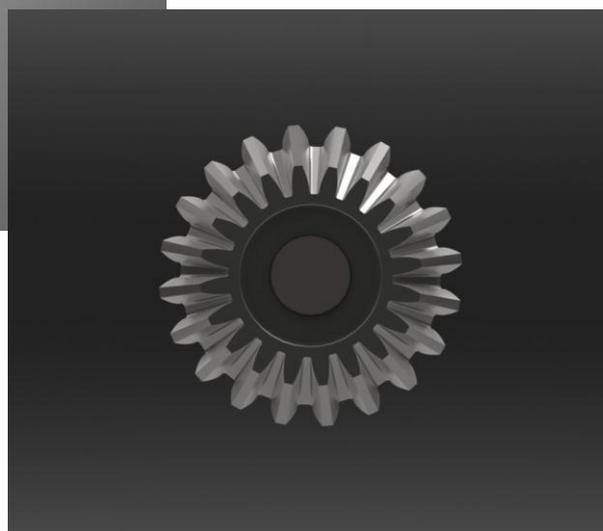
Vista frontale del montaggio asse15mm-ingranaggio
